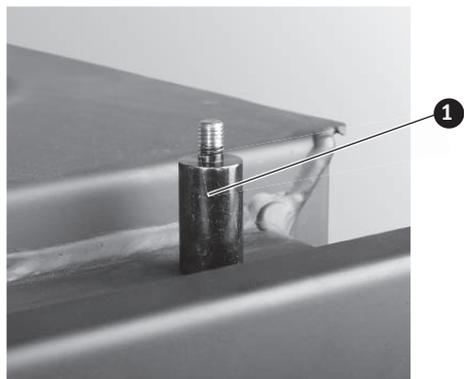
Monter 2 fixations du guidage de gaz de combustion
